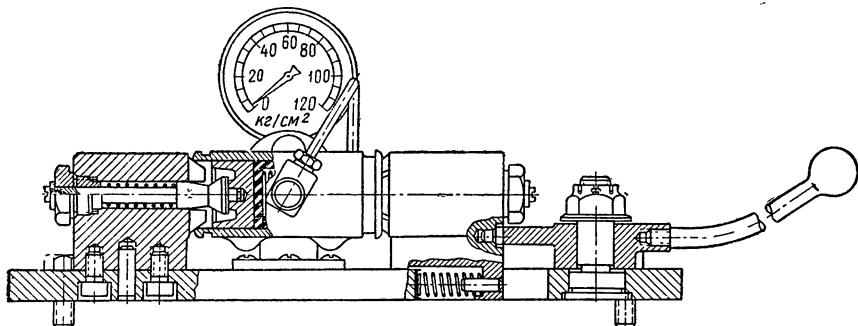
Приспособление для испытания колесных цилиндров заднего тормоза
